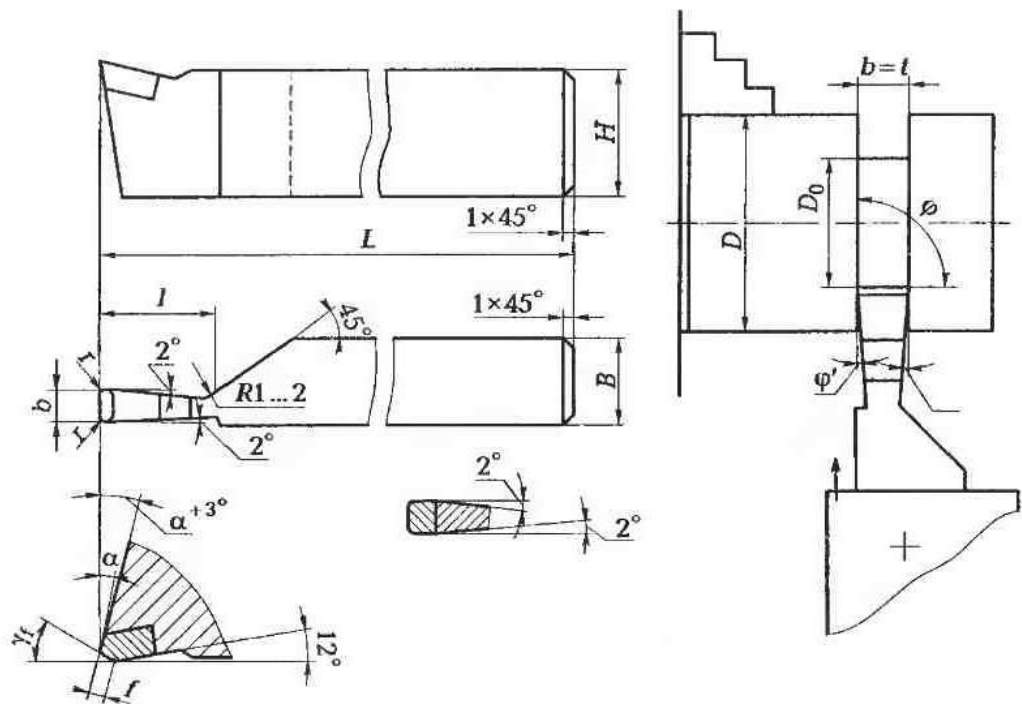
Токарный отрезной резец, оснащенный пластиной из твердого сплава
